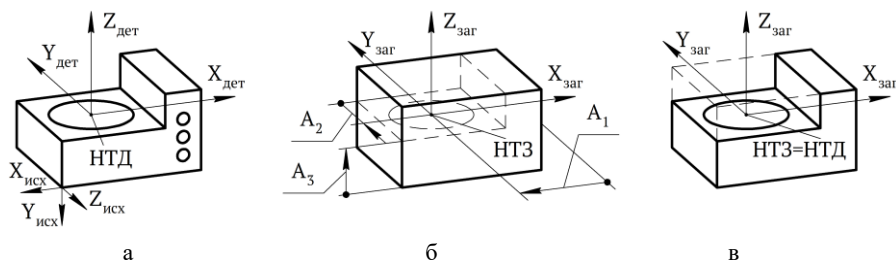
Нулевые точки: а – детали в САПР ТП; б – заготовки на станке до обработки; в – заготовки на станке после обработки
